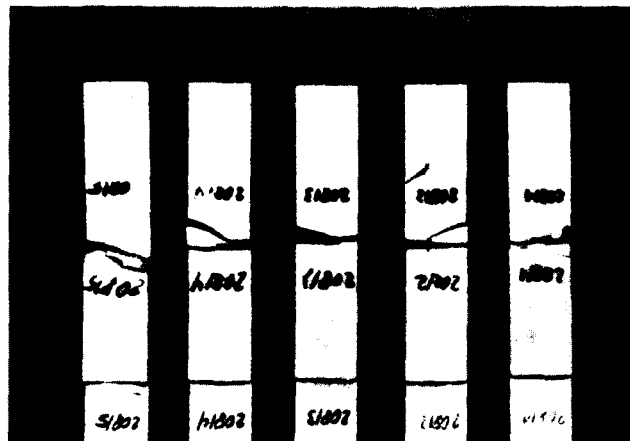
Bruchbilder einseitig gelaschter Proben
